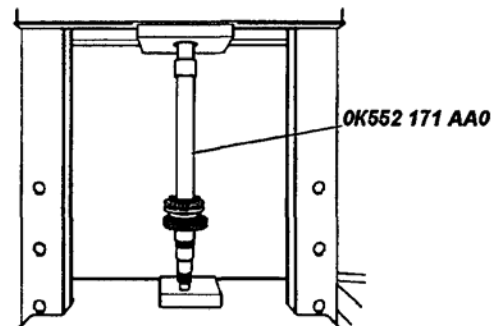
Установка ступицы обоймы синхронизатора 5-ой передачи и заднего хода
